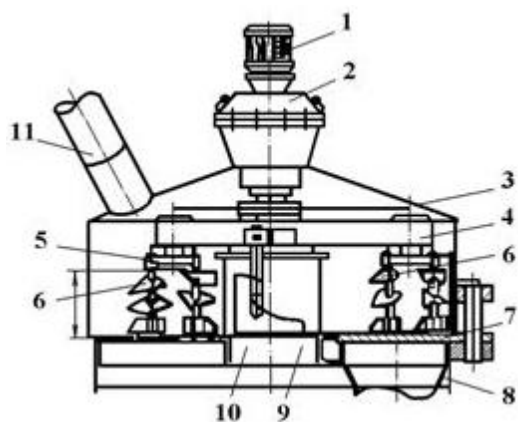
Смеситель для приготовления стекольной шихты: 1 – электродвигатель; 2 – редуктор; 3 – корпус; 4 – траверса; 5 – кронштейн поворота мешалок; 6 – мешалки; 7 – разгрузочный затвор; 8 – выходное устройство; 9 – внутренний стакан; 10 – наружная лопасть; 11 – загрузочное устройство
